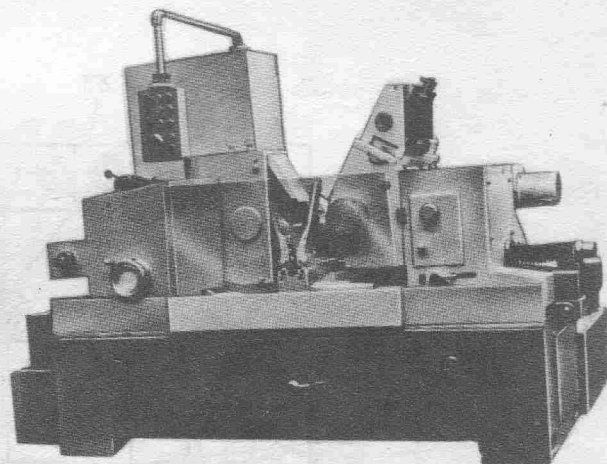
Круглошлифовальный бесцентровый станок ЗМ184
